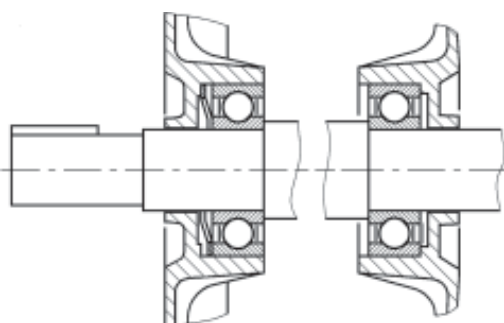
для двигателей габаритов 80 – 132 мм
